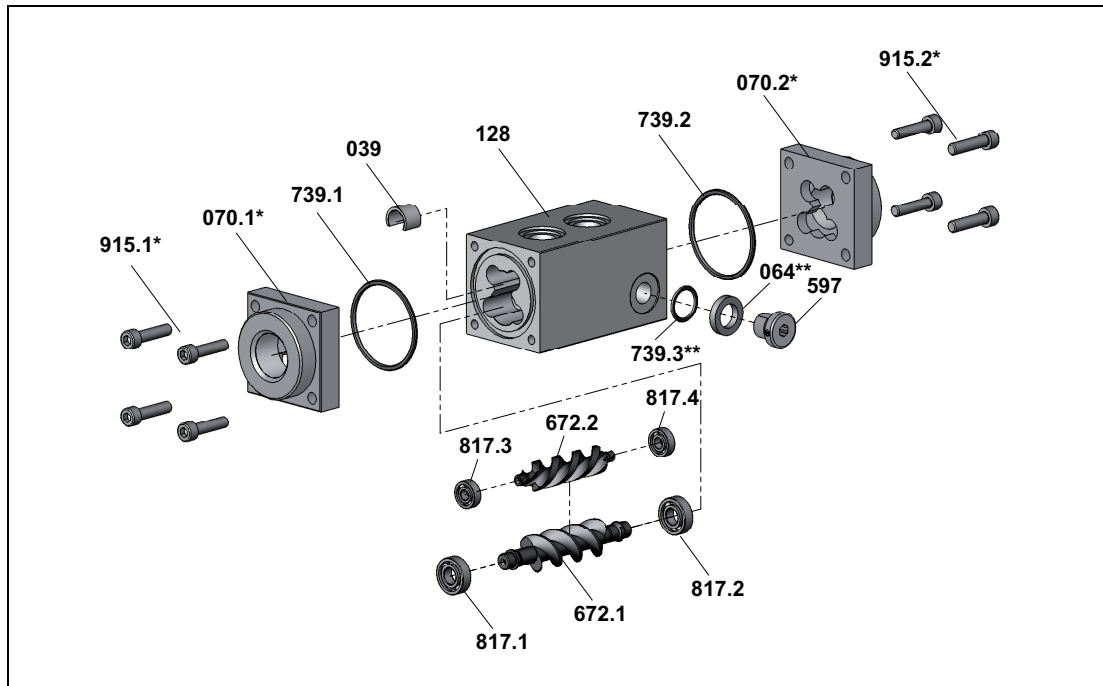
Explosionszeichnung OME 13 – 52 Rohrgewindeanschluss
